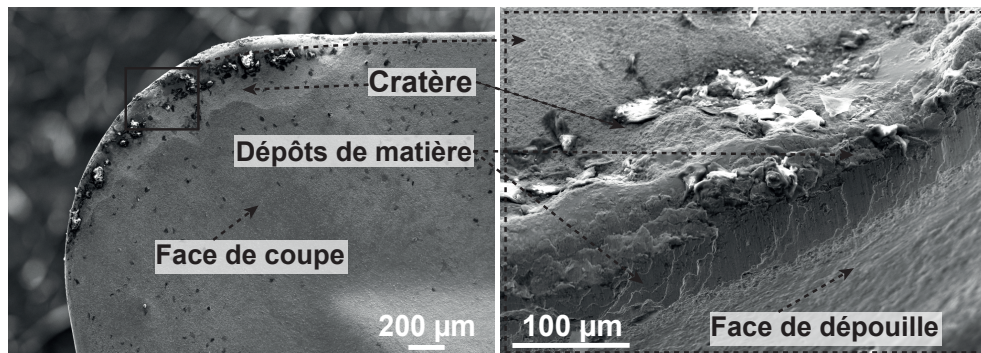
Face de coupe et face de dépouille d'un outil après 20 min d'usinage en finition à la pression de 250 bar
